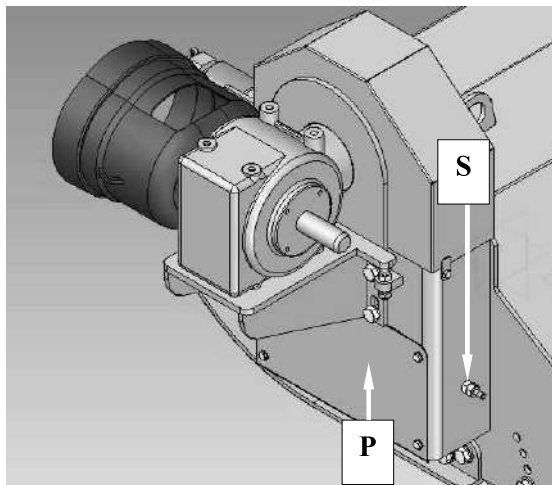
Контроль напряжения клиновых ремней ременной передачи
